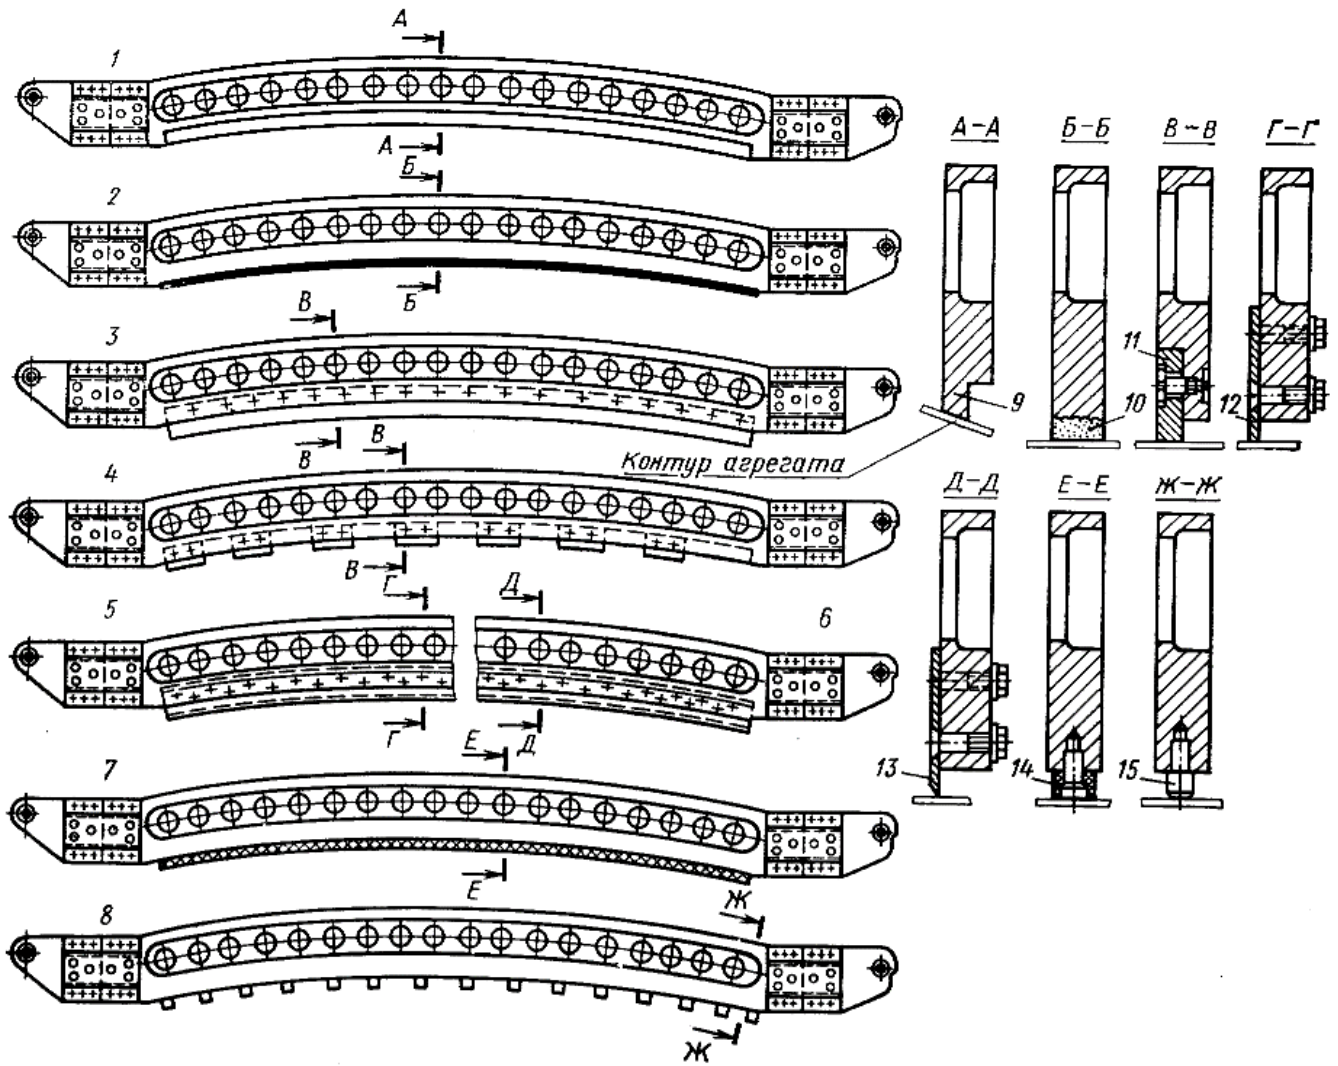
Конструкции рубильников и форма их рабочих поверхностей:
